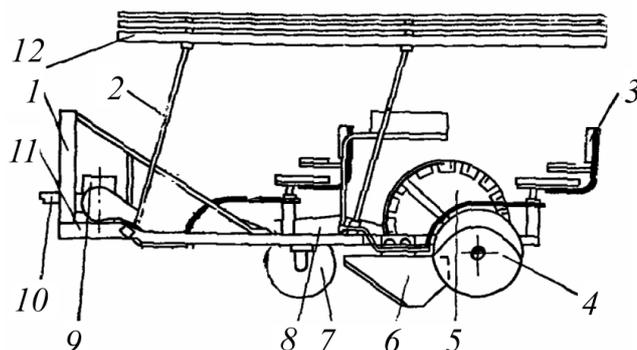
Школьная посадочная машина ЭМИ-5М: 1 – навесное устройство; 2 – каркас; 3 – сидение; 4 – каток прикатывающий; 5 – посадочный аппарат; 6 – сошник; 7 – опорное колесо; 8 – цепная передача; 9 – редуктор; 10 – карданная передача; 11 – рама; 12 – тент
